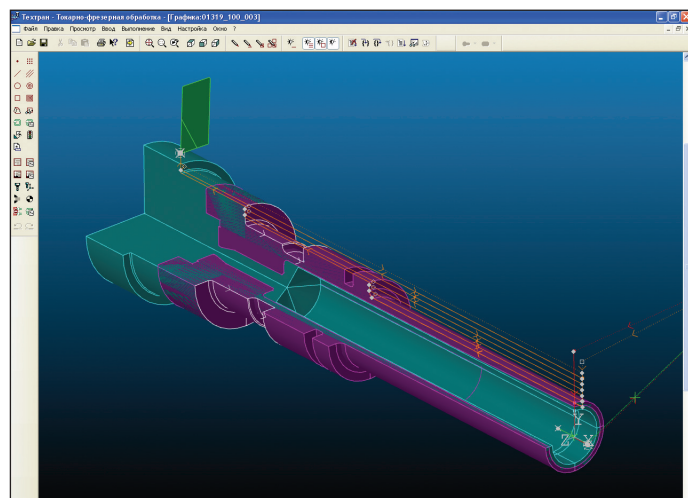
Частичный разрез детали и заготовки (произвольный вид)
